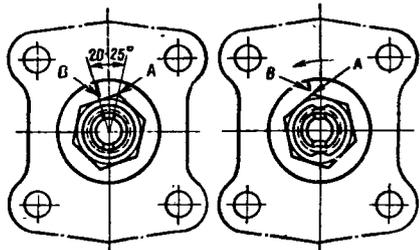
Схема регулировки подшипников ступиц передних колес: А - кромка гайки; В - метка на шайбе. Момент затягивания гайки 0,7 кгс·м. Ослабление гайки на 20-25°
